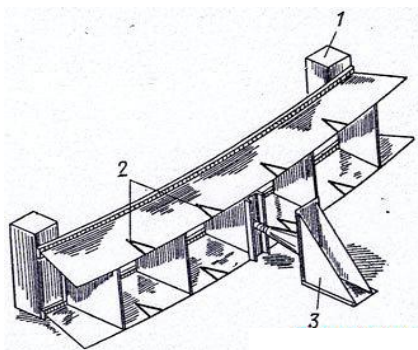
Термомеханическая правка сварного фундамента с применением домкрата (цифрами показана последовательность мест нагрева): 1 – опоры; 2 – места нагрева; 3 – домкрат
